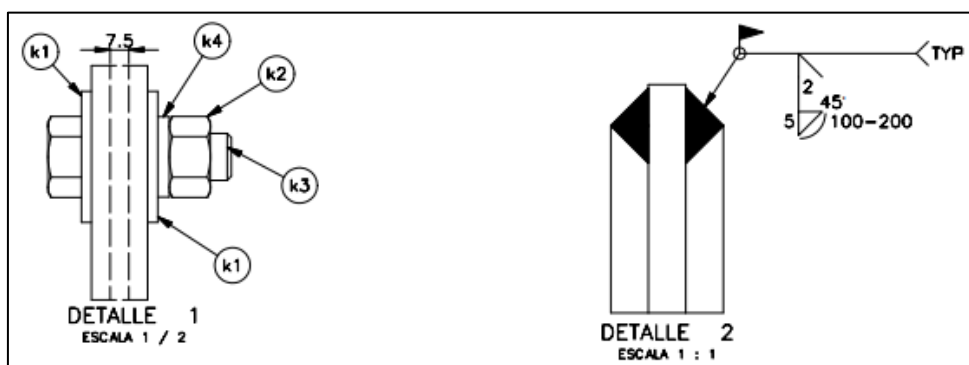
Vista de pernos de sujeción y soldadura
